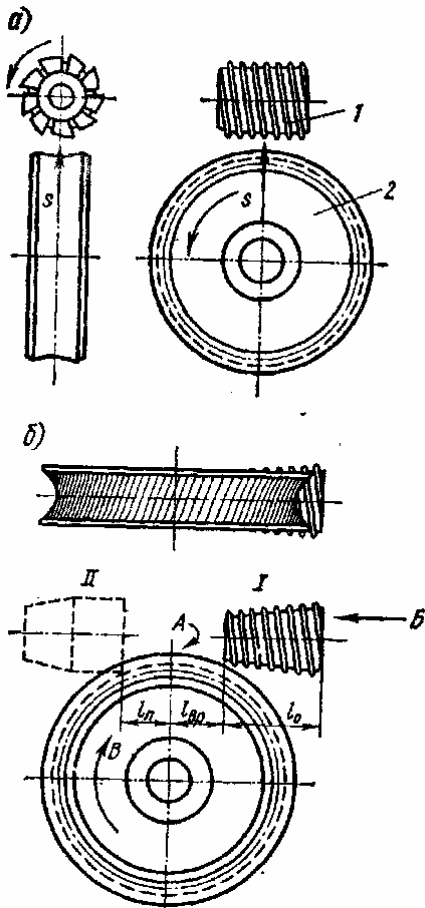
Зубонарезание червячных зубчатых колес червячными фрезами: а – способом радиальной подачи; б – способом тангенциальной подачи; I-II – соответственно начальное и конечное положения фрезы
